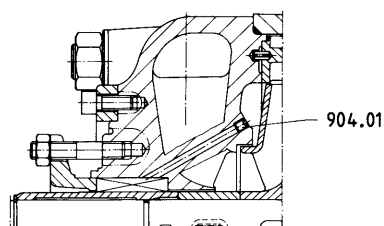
Baugrößen L 25/32/40/50/65, ungekühlte Packungsstopfbuchse, Ausführung U1AA, saufseitig ohne Sperrung, druckseitig ohne Druckentlastung
